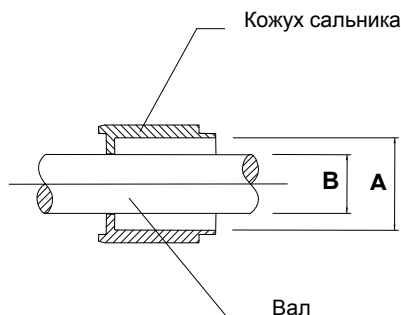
размеры А и В вала и кожуха уплотнения вала
